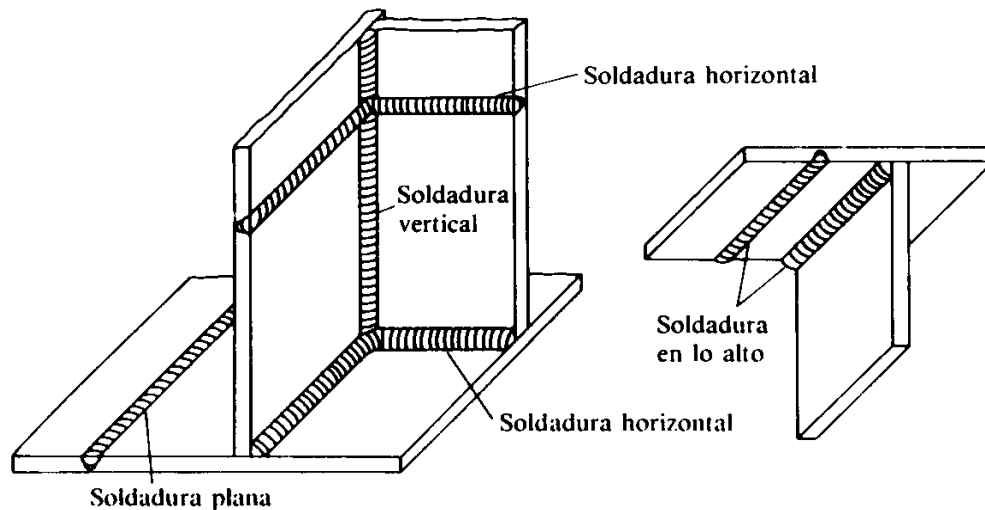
Clasificación de las soldadura por su posición.
